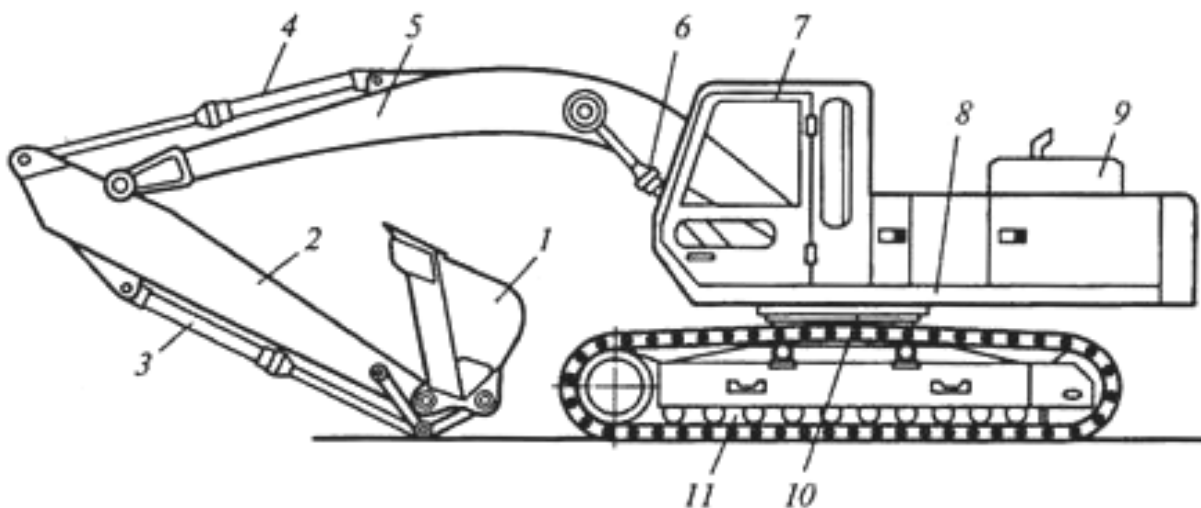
Одноковшовый полноповоротный гусеничный экскаватор ЕК-270: 1 – ковш; 2 – рукоять; 3, 4, 6 – гидродомкраты; 5 – стрела; 7 – кабина оператора; 8 – поворотная платформа; 9 – силовая установка; 10 – опорно-поворотное устройство; 11 – гусеничное ходовое устройство
